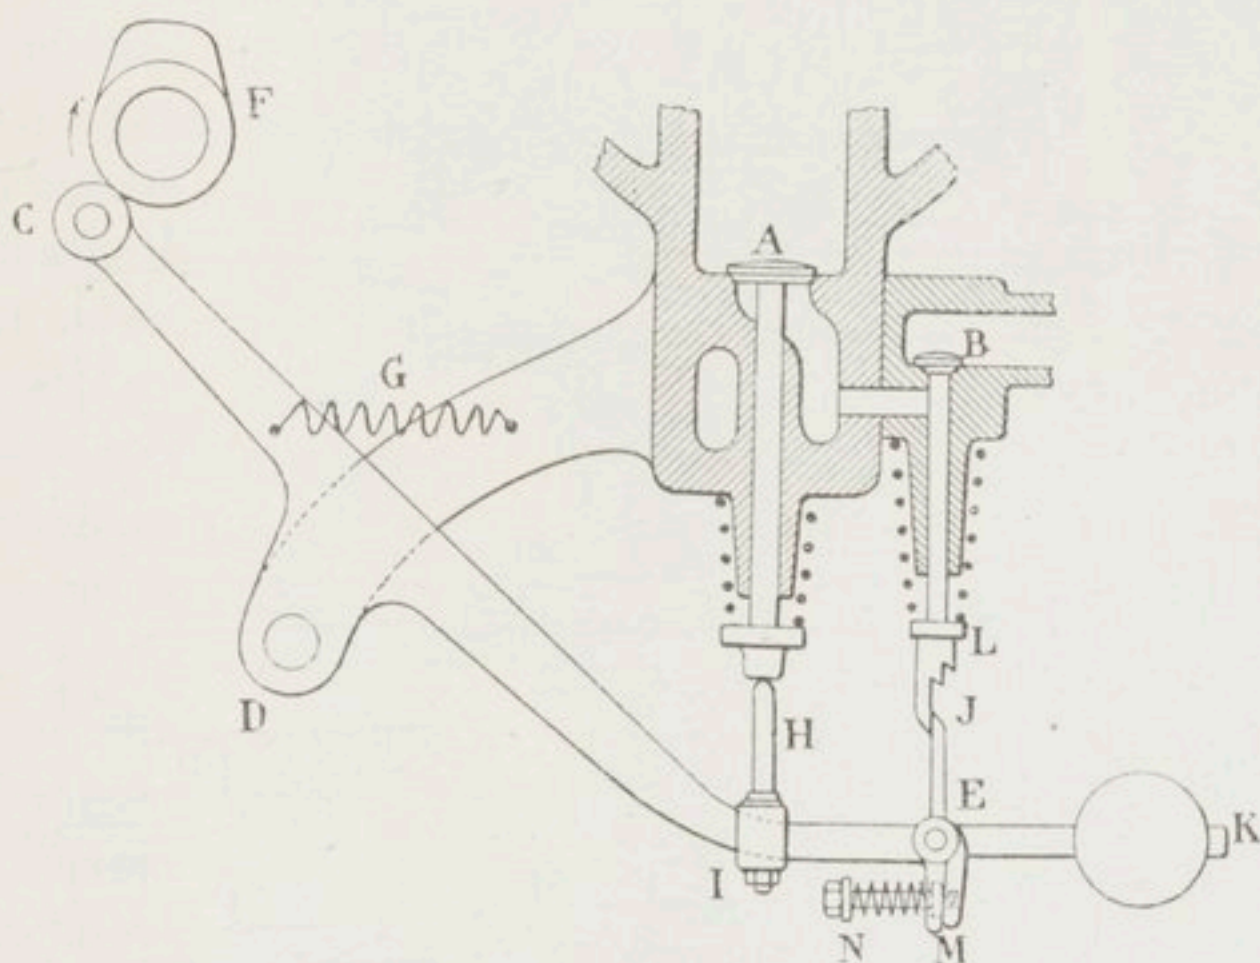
Régulateur pendulaire du moteur Crossley.
